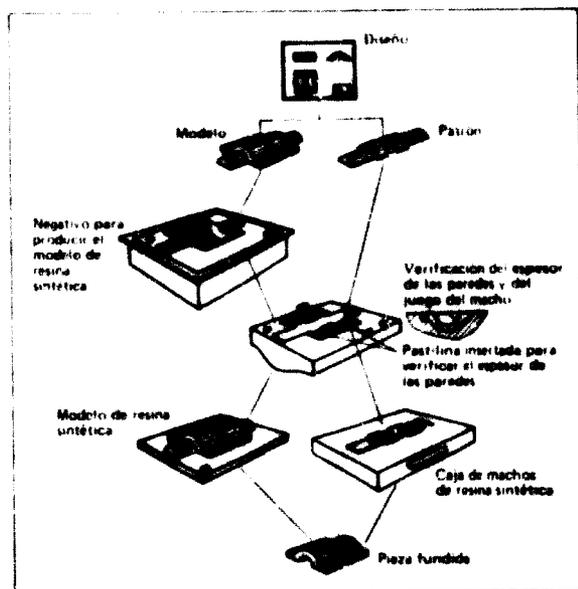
Plan de inspección para las piezas fundidas de resina sintética.
